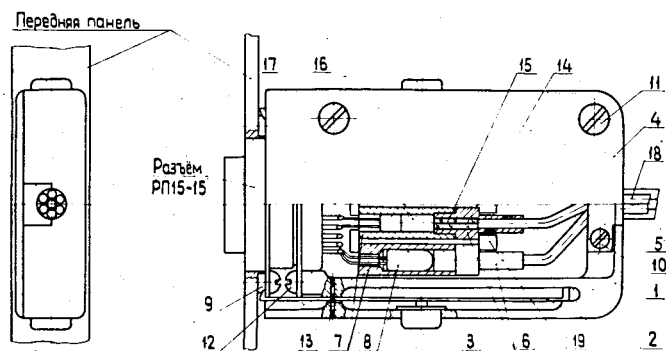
Многоконтактный активный разъёмный соединитель на базе электрического разъёма РП-15-15: (1 – корпус; 2 – пластинчатая пружина; 3 – кнопка; 4 – крышка корпуса; 5 – фиксатор ВОК; 6 – втулка; 7 – втулка для оптического компонента; 8 – светодиод; 9, 13 – элементы крепления; 14 – ОВ; 15 – капилляр; 16 – фотодиод).
